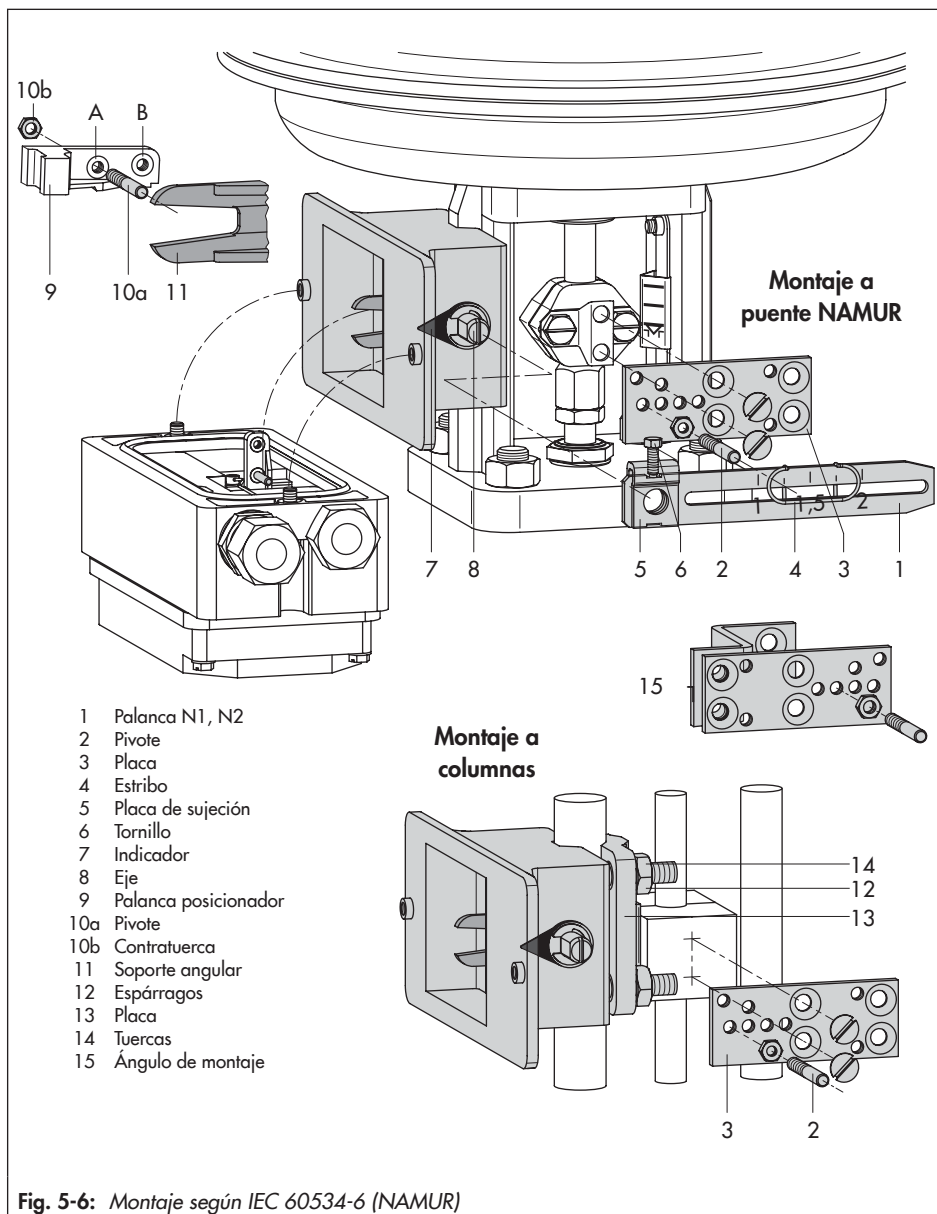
Montaje según IEC 60534-6 (NAMUR)
